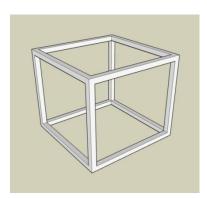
Estructura. FUENTE: Elaboración Propia.
